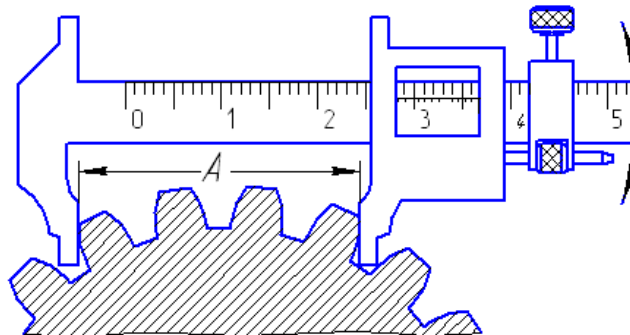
Вимірювання товщини зубця штангенциркулем
